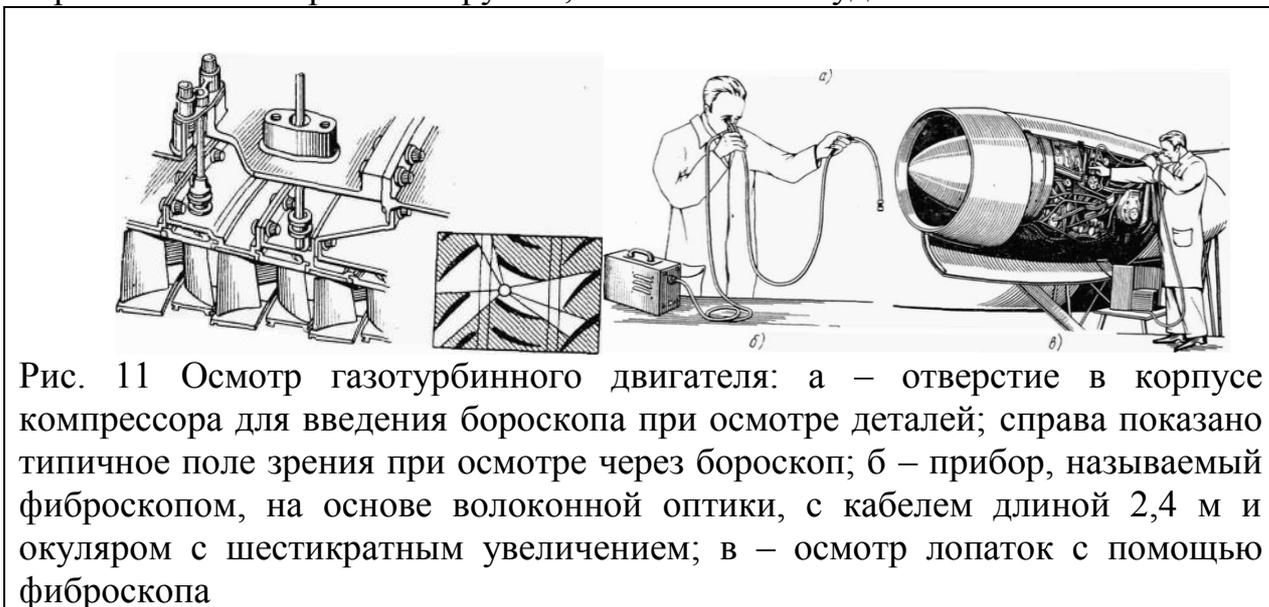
Осмотр газотурбинного двигателя: а – отверстие в корпусе компрессора для введения бороскопа при осмотре деталей; справа показано типичное поле зрения при осмотре через бороскоп; б – прибор, называемый фиброскопом, на основе волоконной оптики, с кабелем длиной 2,4 м и окуляром с шестикратным увеличением; в – осмотр лопаток с помощью фиброскопа
